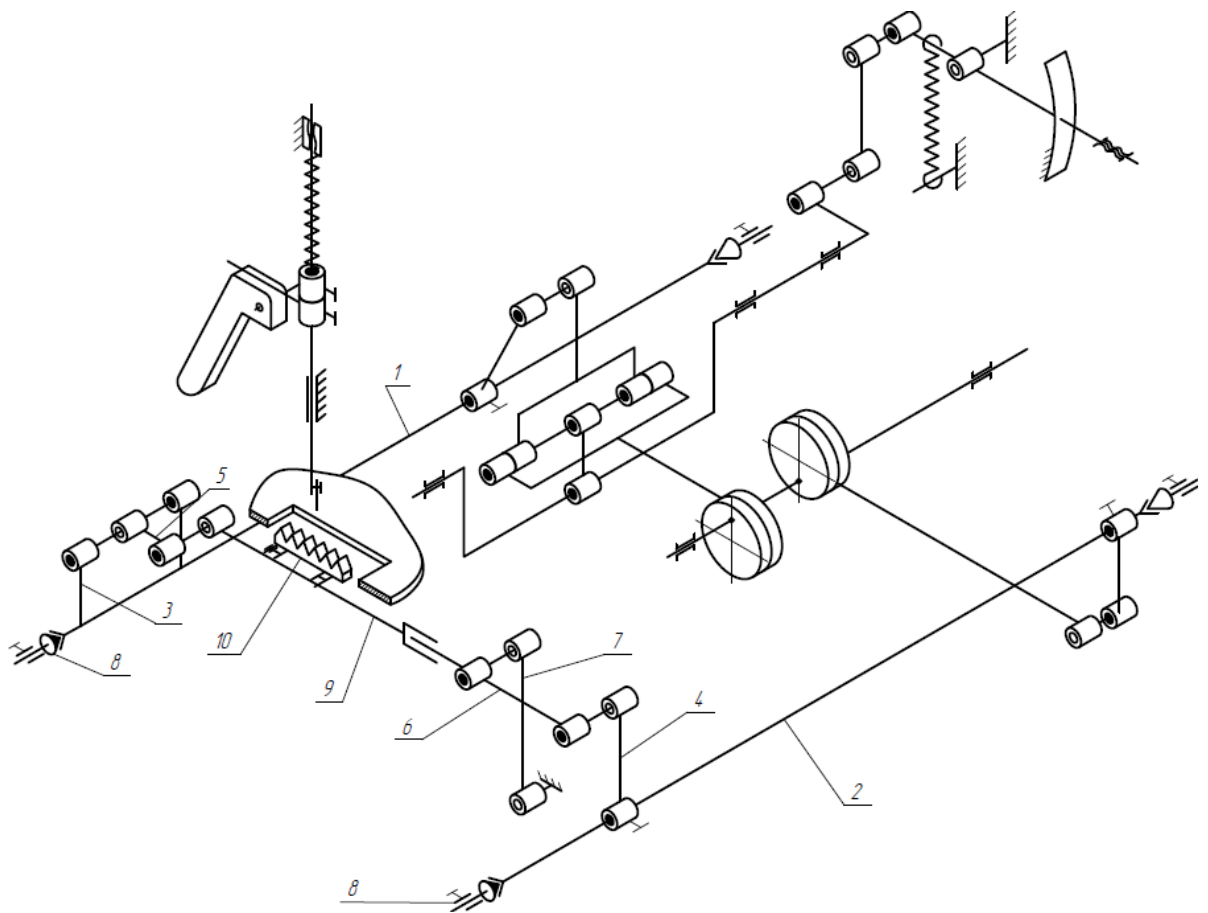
Кінематична схема нового механізму зубчастої рейки
